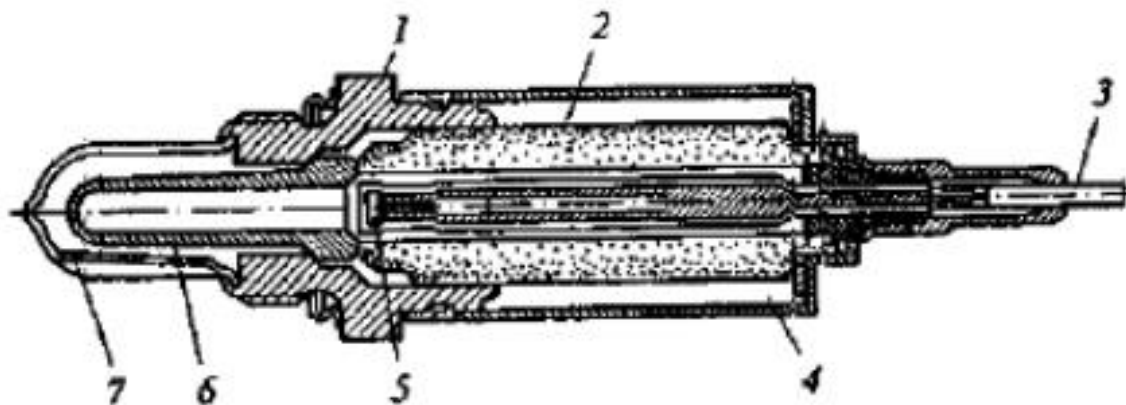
Датчик кислорода: 1 и 2 – соответственно металлический и керамический корпуса; 3 – выходной кабель; 4 – внешний кожух; 5 – контактный наконечник; 6 – активный элемент (колпачок); 7 – защитный кожух с прорезями
